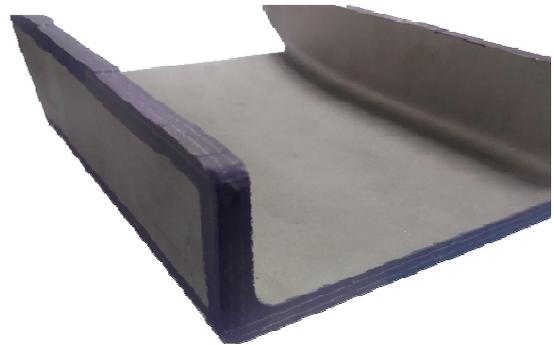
某铸件机加工余量线 Fig.3 Machining allowance line of a casting
